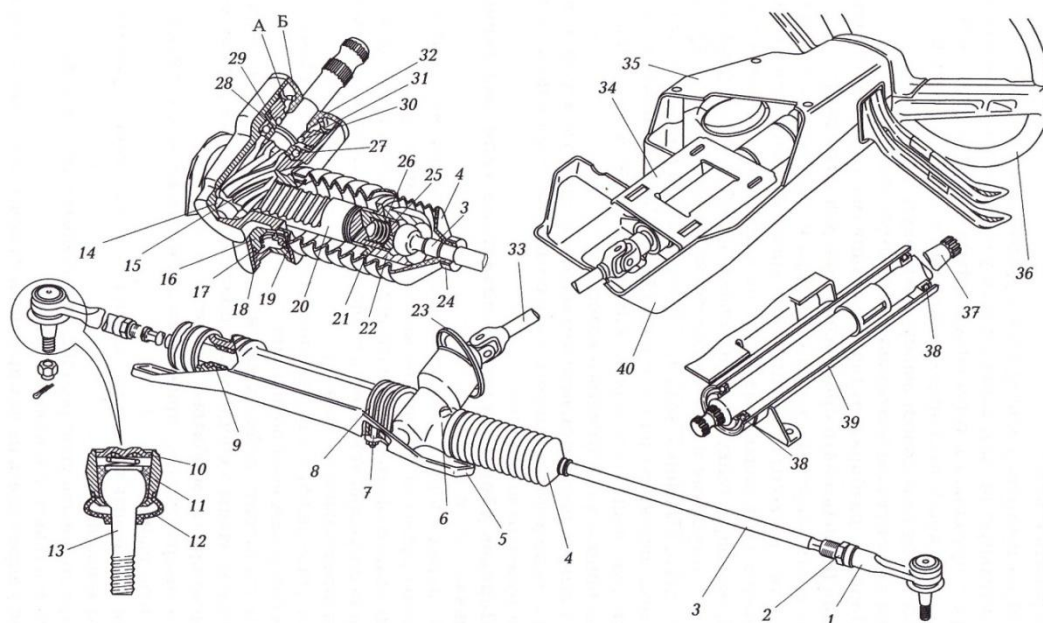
Рулевой механизм типа «зубчатое колесо - рейка»:
